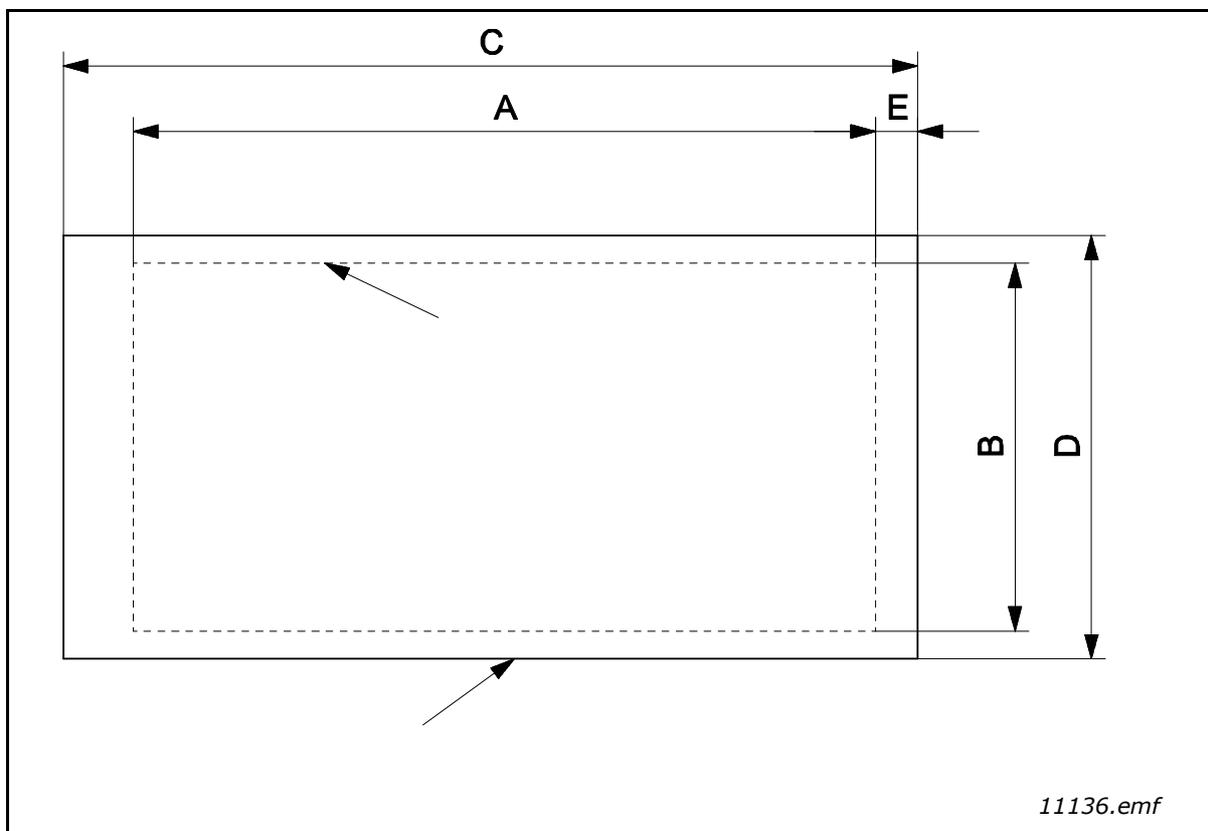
Dimensiones de corte del montaje con bridas de MR4 a MR9
